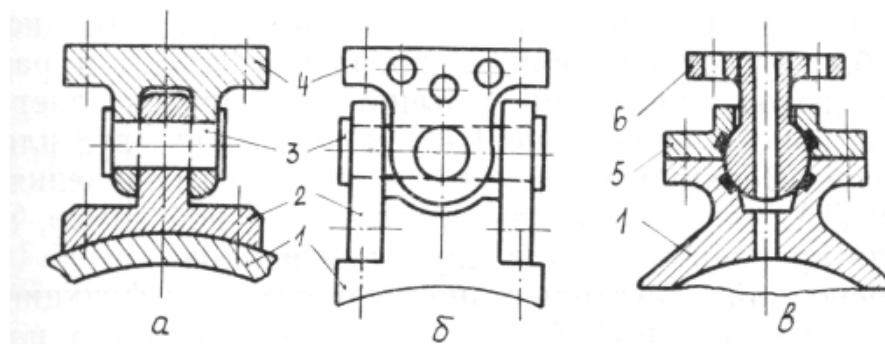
Схемы конструкции креплений поворотных камер:
